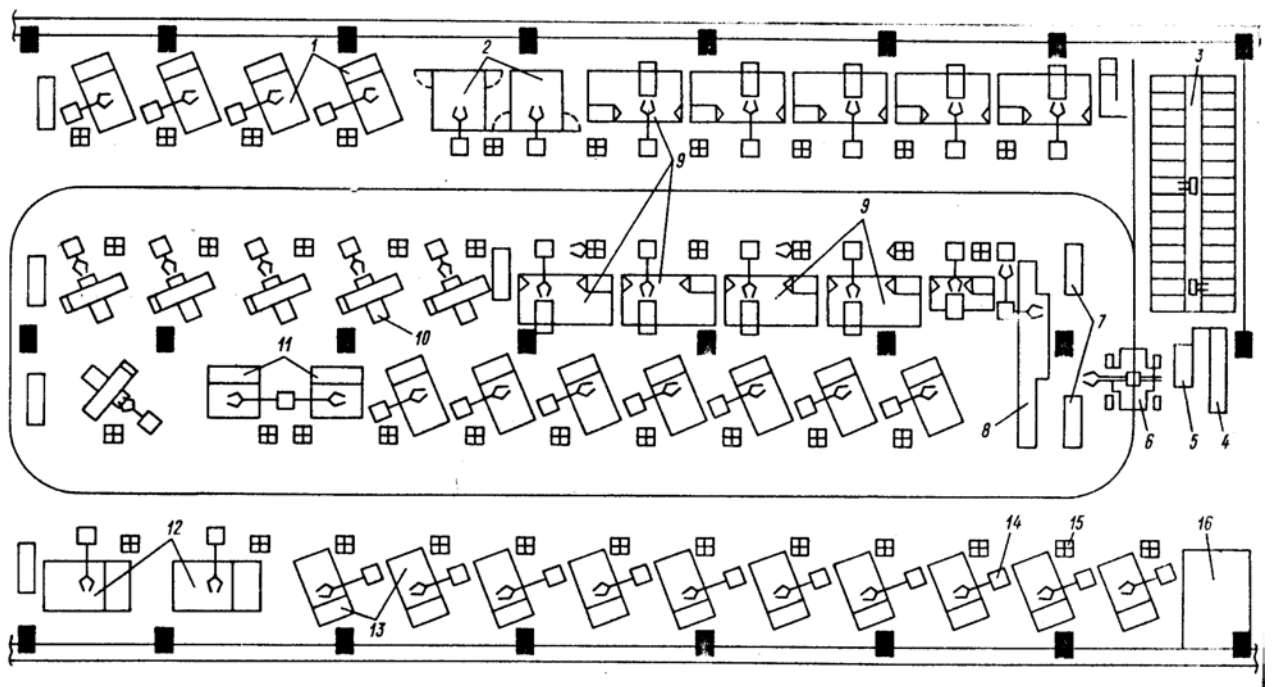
Роботизированный цех механообработки: 1, 2, 11, 12, 3 — токарные станки; 3 — склад; 4 — загрузочное устройство; 5 — разгрузочное устройство; 6 — напольные транспортные ПР; 7 — промежуточные склады; 8 — протяжной станок; 9 — шлифовальные станки; 10 — фрезерные станки; 14 — ПР; 15 — магазины; 16 — пульт диспетчера
